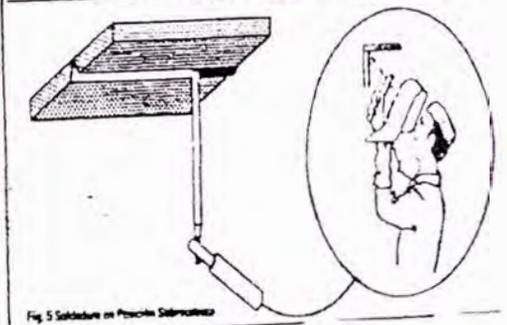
Soldadura en Posición Sobrepuesta
